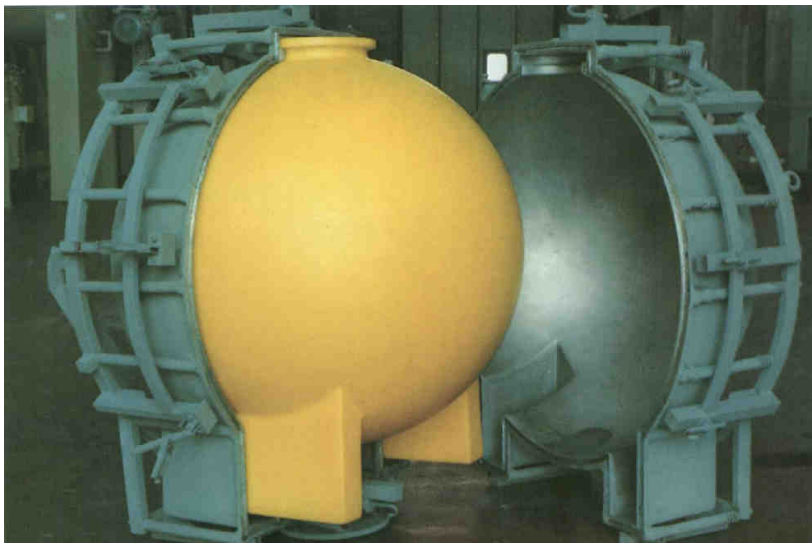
Molde de aluminio para moldeo rotacional. [2]
